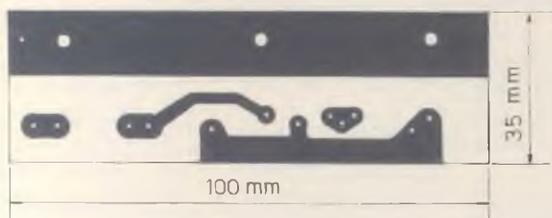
Disegno del circuito stampato necessario per la realizzazione del cablaggio del regolatore di tensione; questo circuito dovrà essere costruito nelle dimensioni qui sopra riportate.
